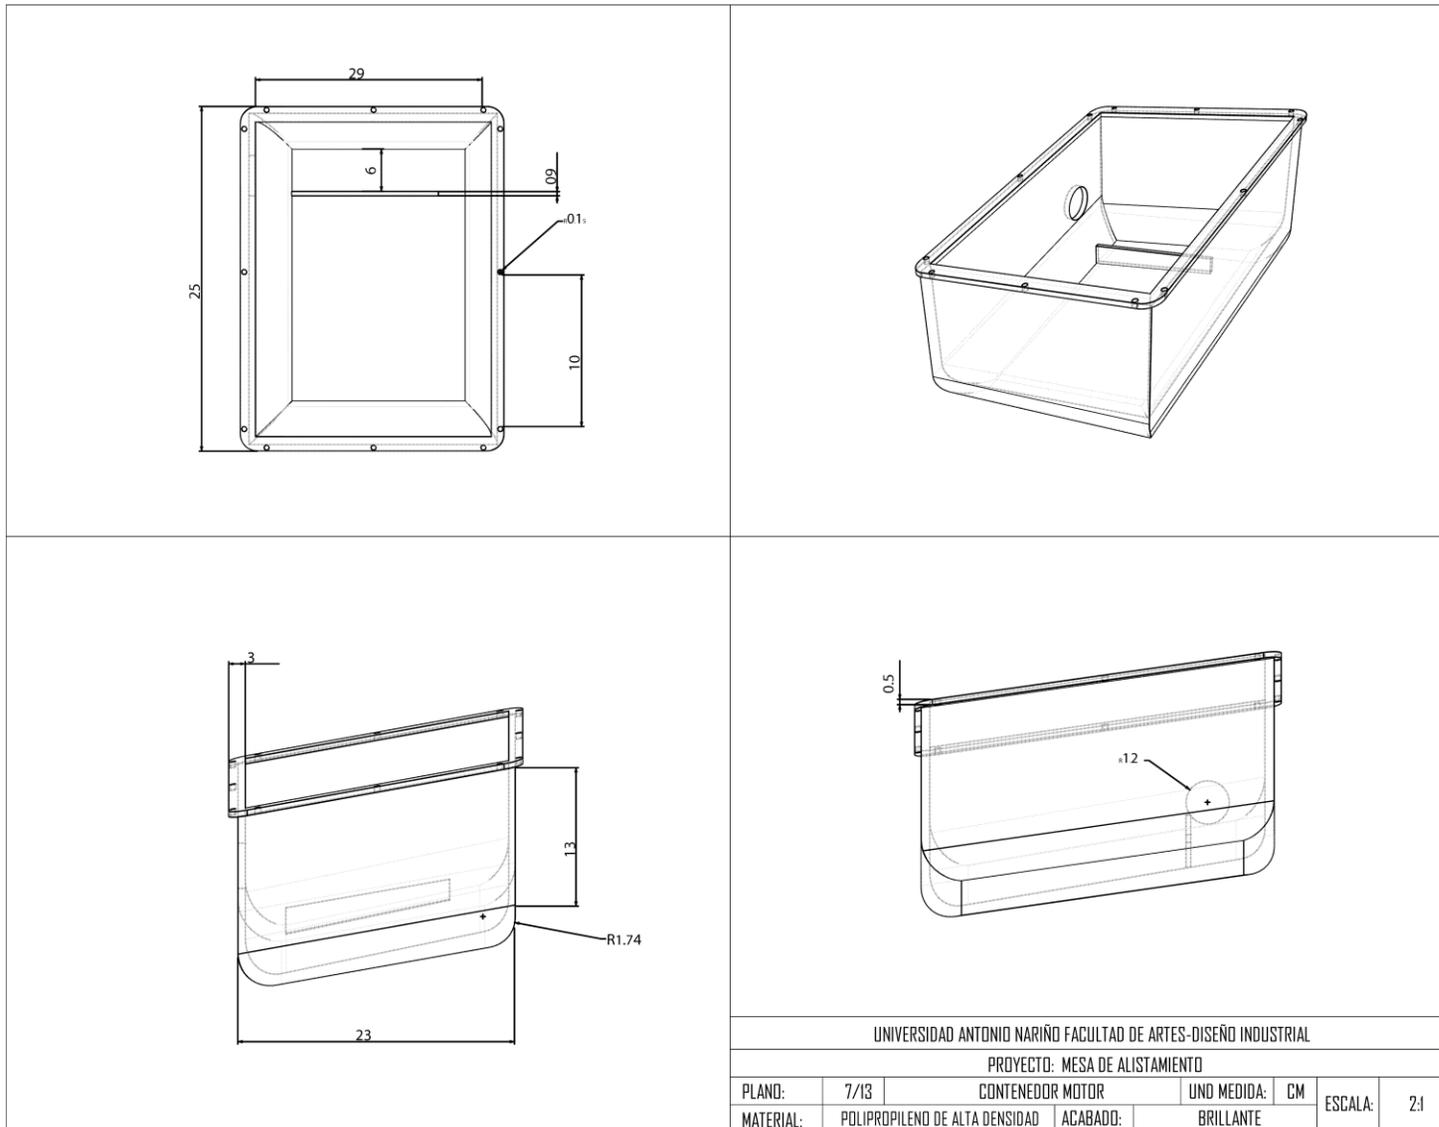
Planos piezas 6 (Elaboración propia, 2020)
